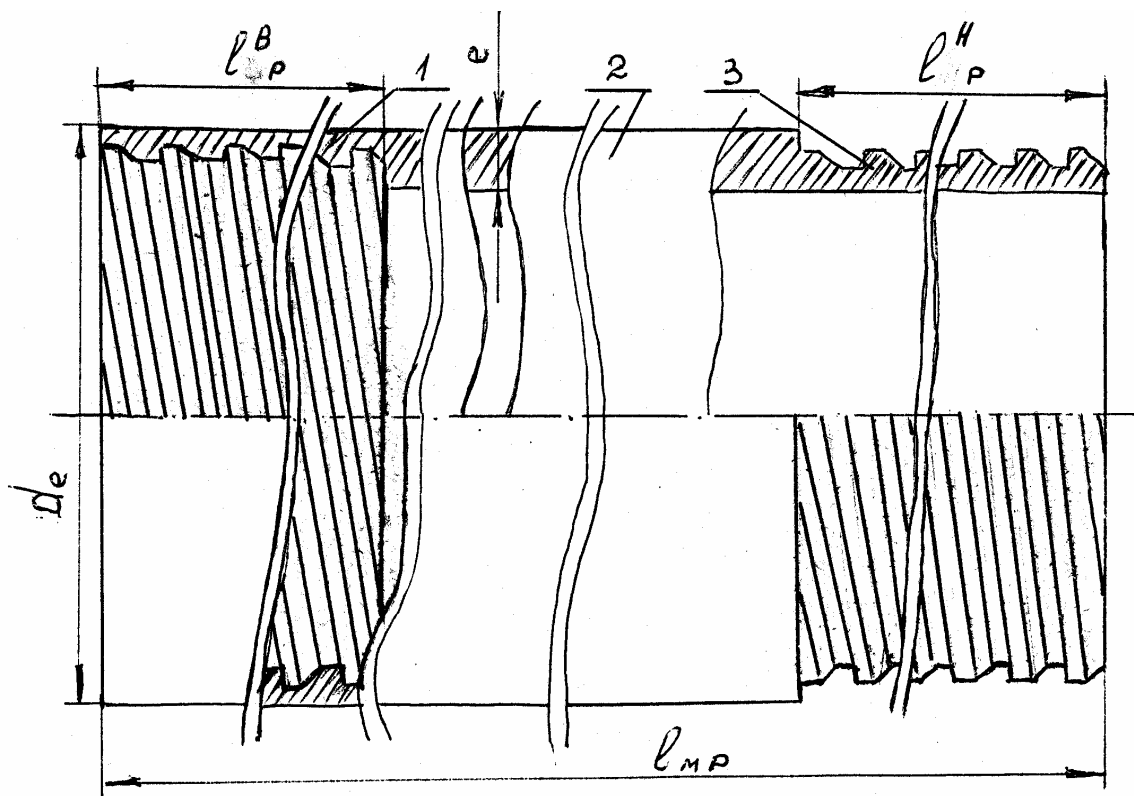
Схема полиэтиленового трубного модуля с резьбами
